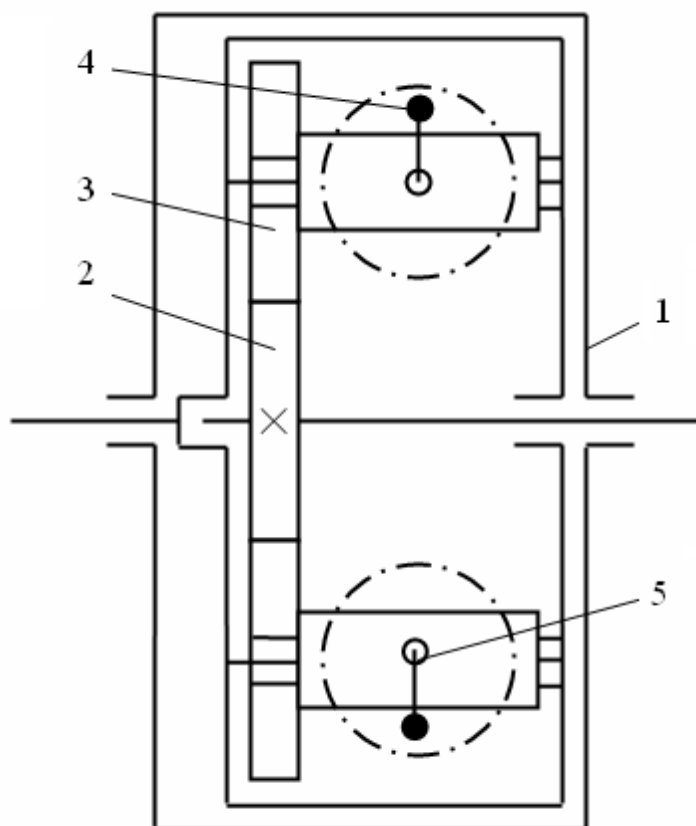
Схема ошибочной конструкции инерционной передачи без механизмов свободного хода
